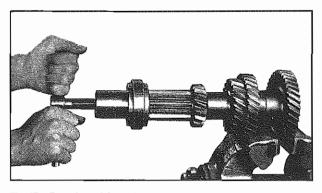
Estrazione del cuscinetto Pulling off roller bearing
